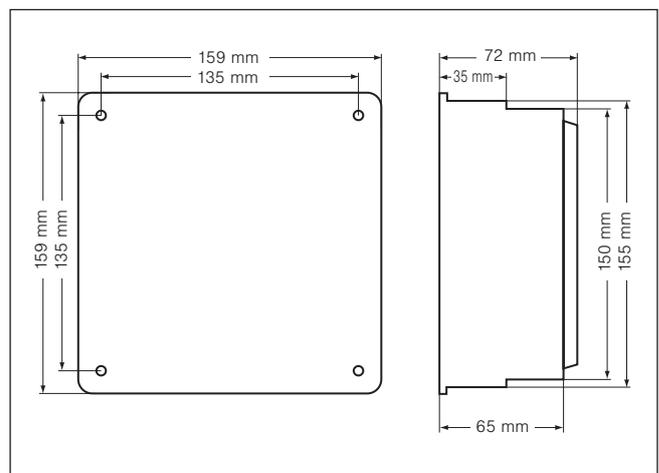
Abmessungen UP-Gehäuse für Dimmkaktor 2D
